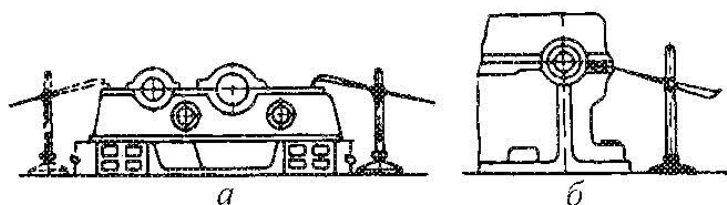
Вивірювання заготовок у горизонтальній площині при установці на розточувальних верстатах
